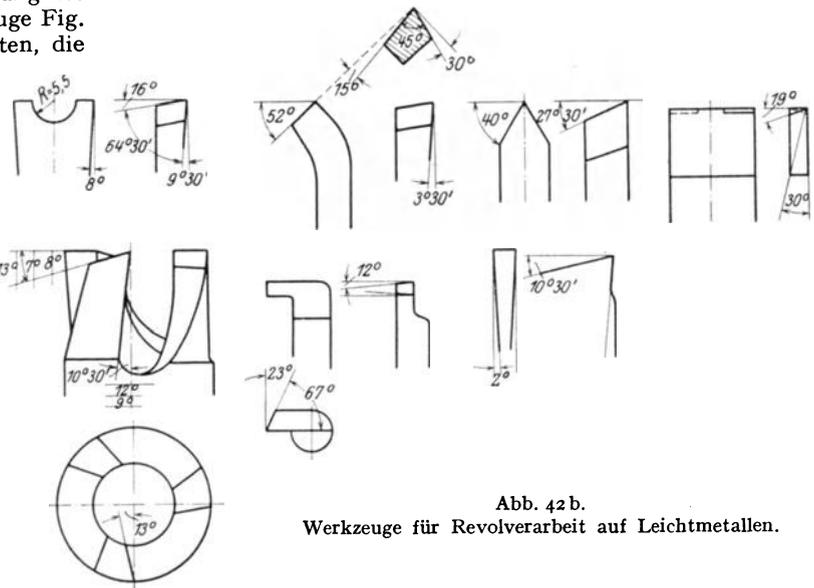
Werkzeuge für Revolverarbeit auf Leichtmetallen.
